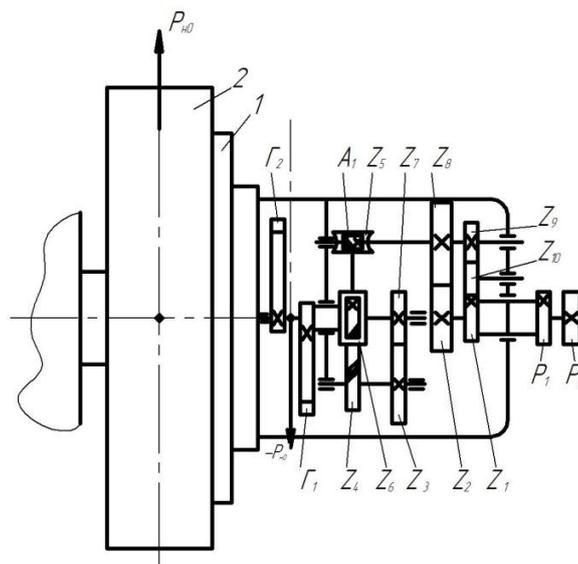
Балансирующее устройство шлифовального станка с ручным приводом
